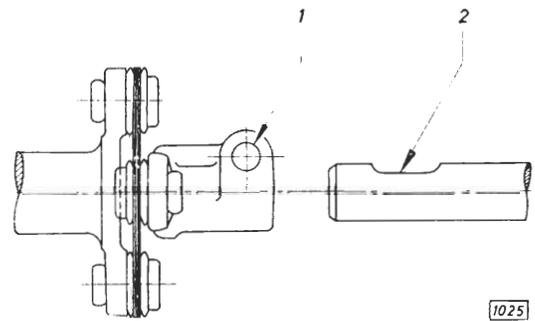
Lage der Lenkspindel zum Lenkspindelflansch
